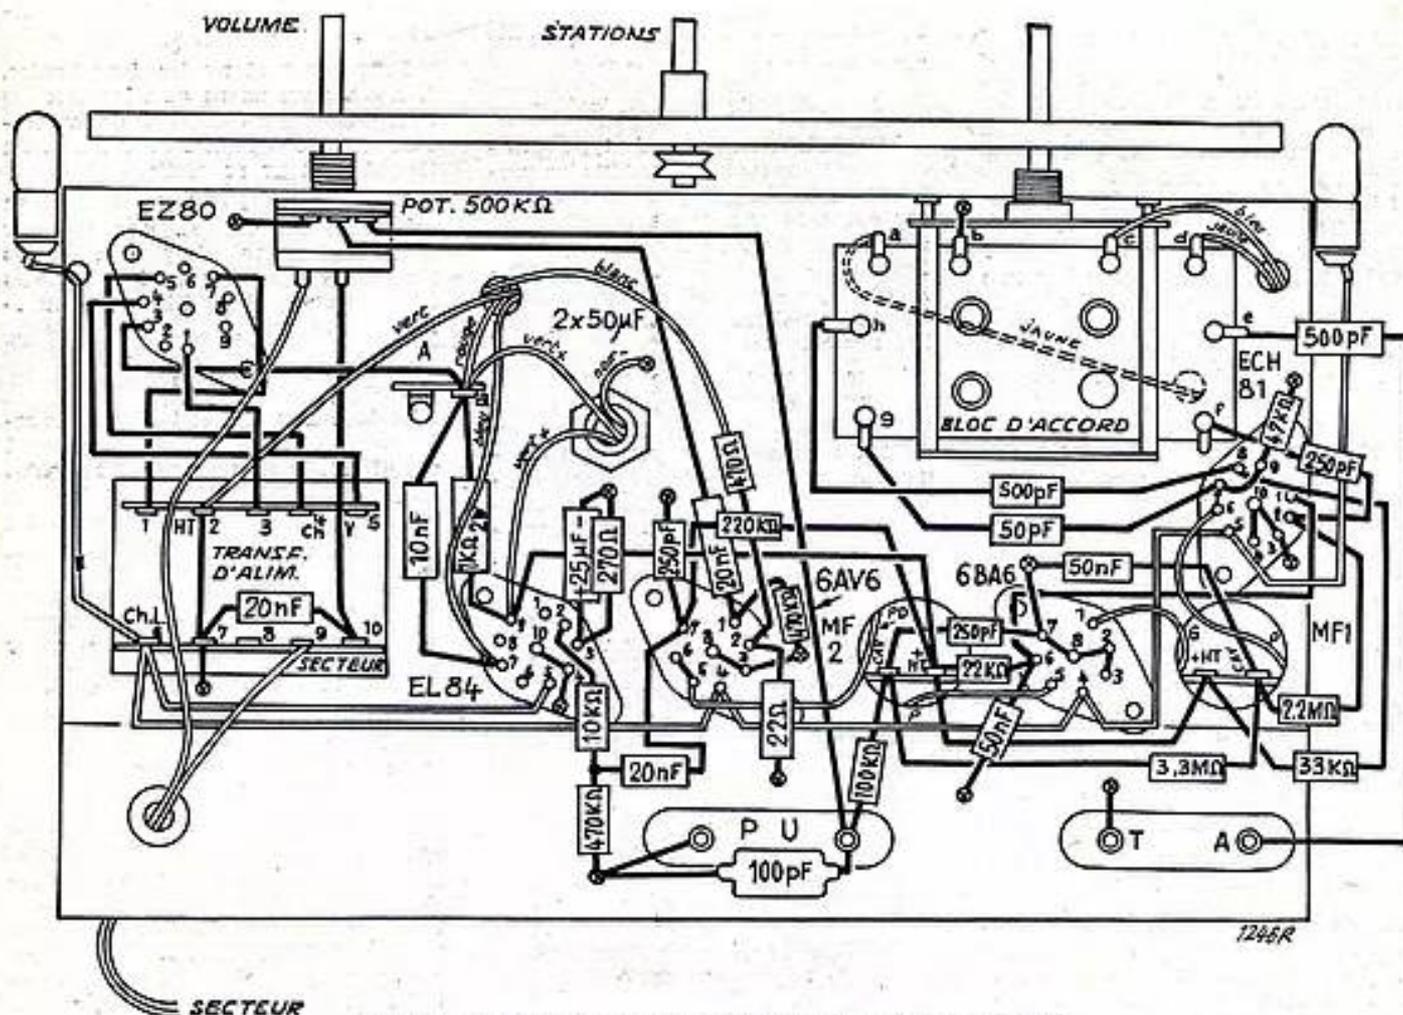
Dessous du châssis (disposition des pièces et câblage).
